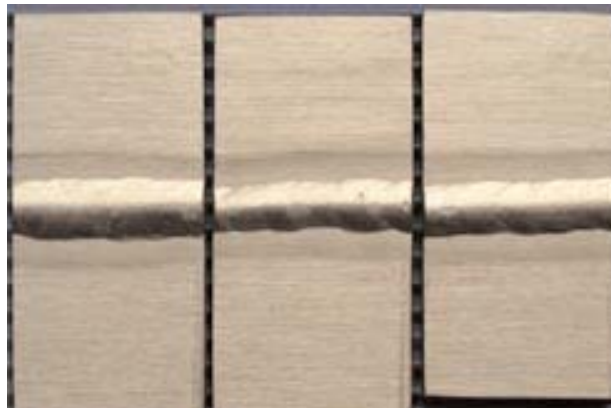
Inconel 622 soldado com INCO-WELD 686CPT (THORTON & COOPER, 2004).
